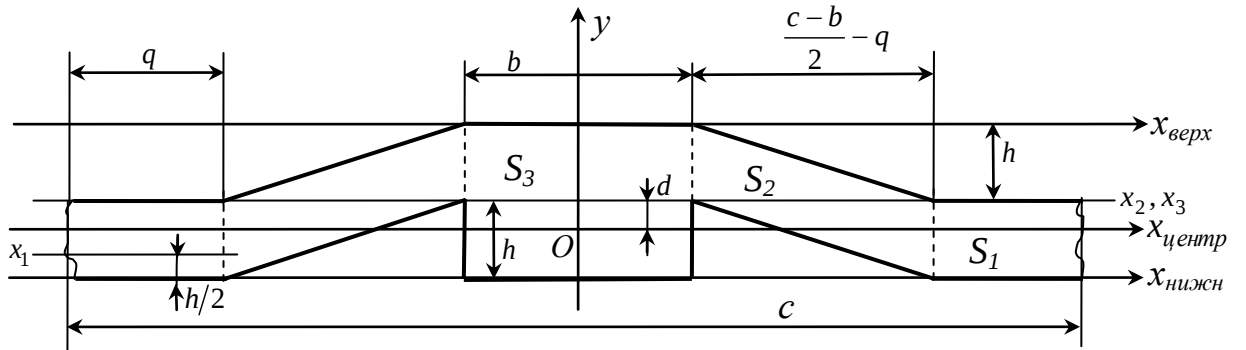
Схема соединительного шва, расположенного с изнаночной стороны
